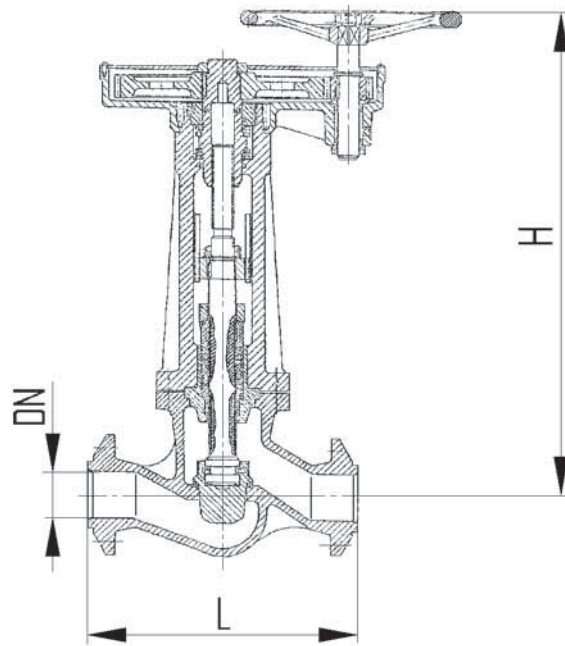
Клапан дроссельный проходной фланцевый с ручным управлением
